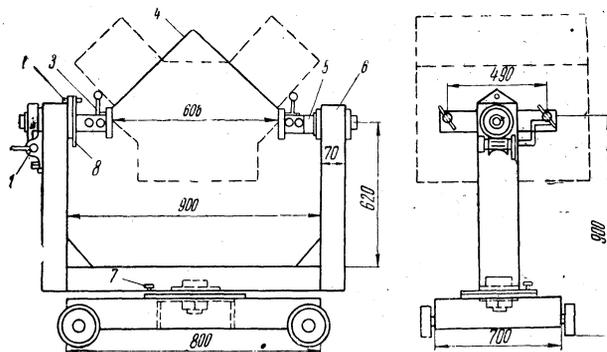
Стенд для разборки и сборки двигателей ЯМЗ-236:
